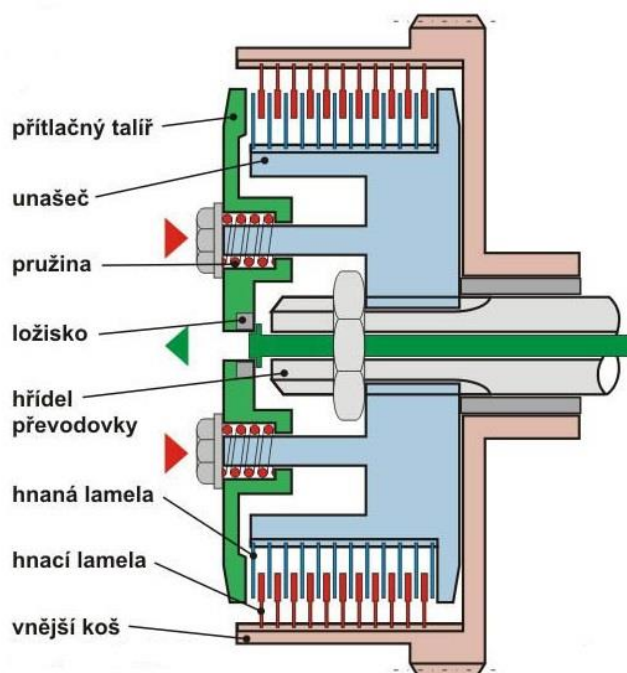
Kompletní sestava dvoukotoučové spojky [33]
